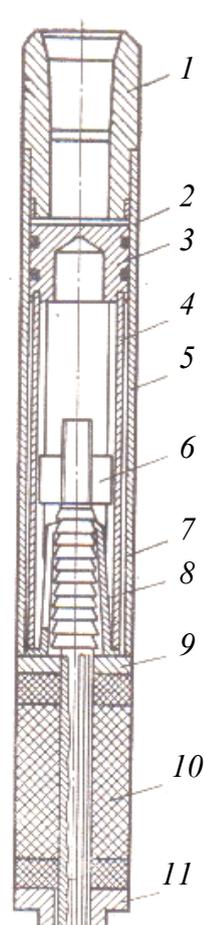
Механизм постановки пакерного уплотнения (МПУ)
